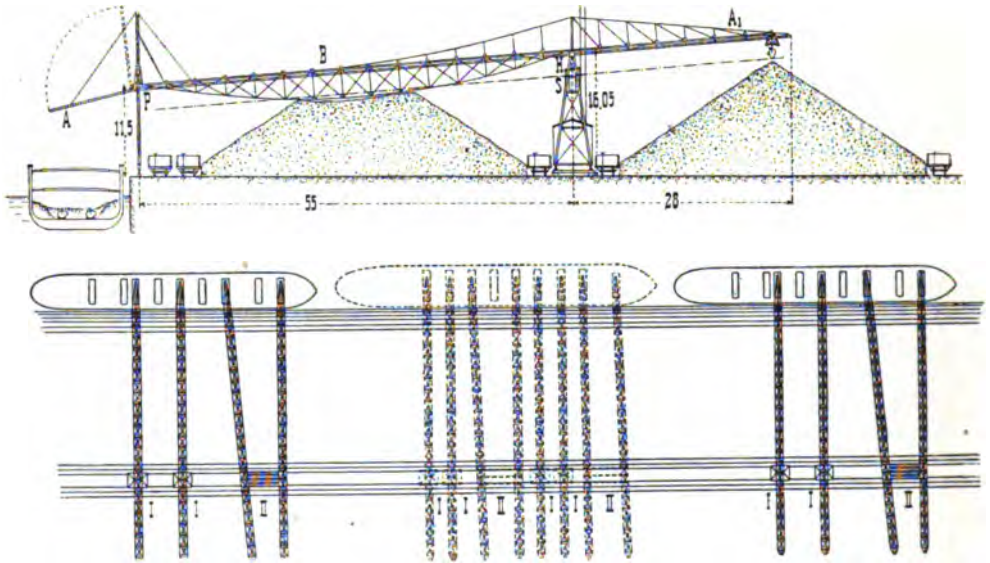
u. 343. Hochbahnkrane der Brown Hoisting and Conveying Machine Co. in Cleveland (Ohio). Masse in m
